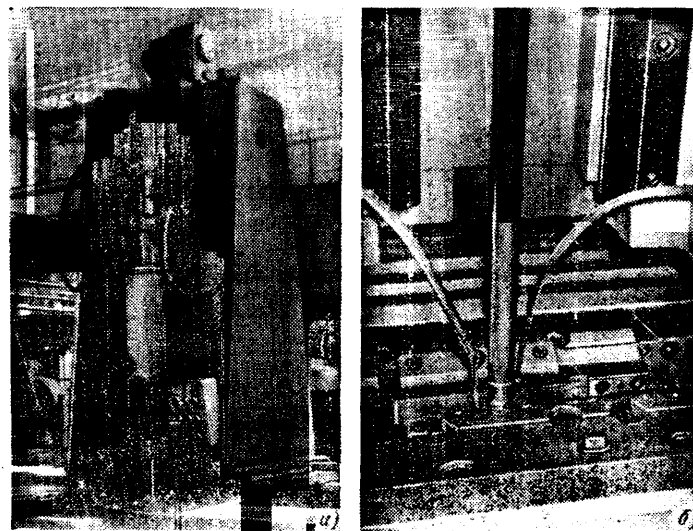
Станок мод. 597 для накатывания эвольвентных шлицев: а — общий вид станка; б — зона обработки
